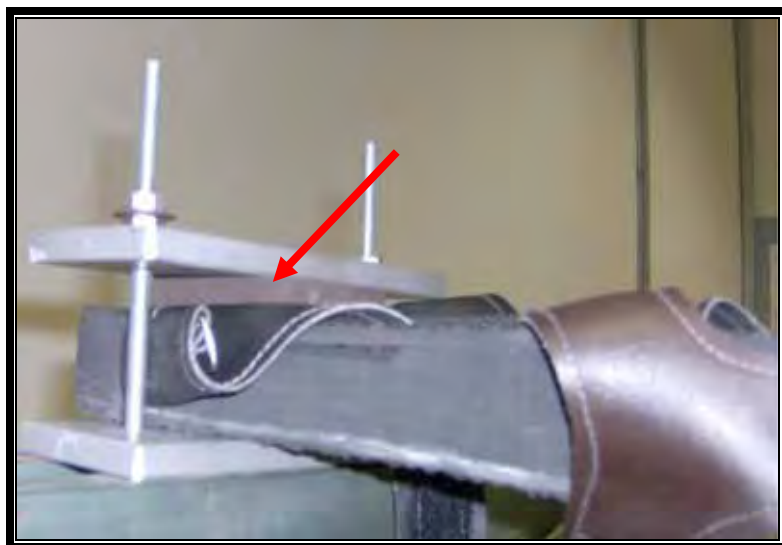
Borracha colocada sobre a sandália e abaixo da barra superior.
